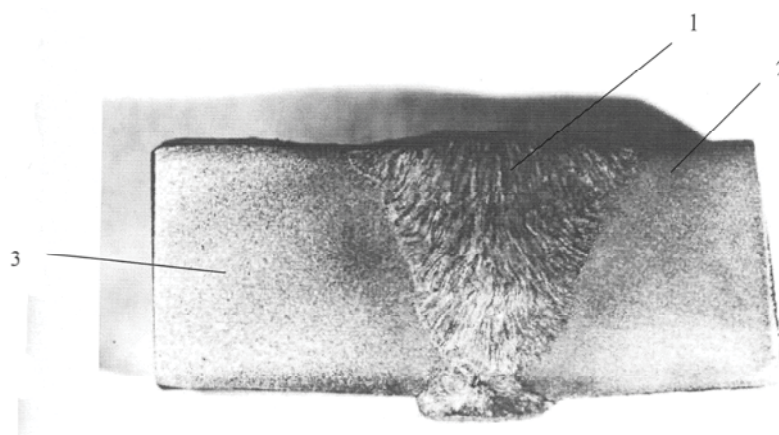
Макроструктура сварного соединения, х1,1. Основной металл – сталь 12X1МФ: 1 – металл шва; 2– металл участков зоны термического влияния; 3 – основной металл. Полуавтоматическая сварка в среде  $\text{CO}_2\text{Ar}$
